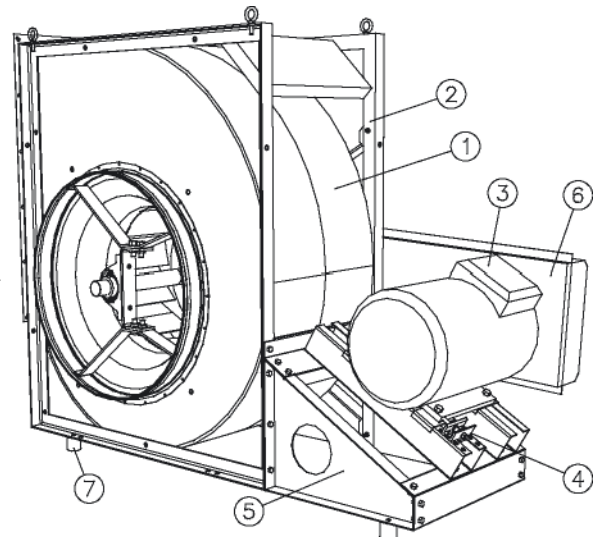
Elementos del ventilador GT-3 (dimensiones 080...100).
